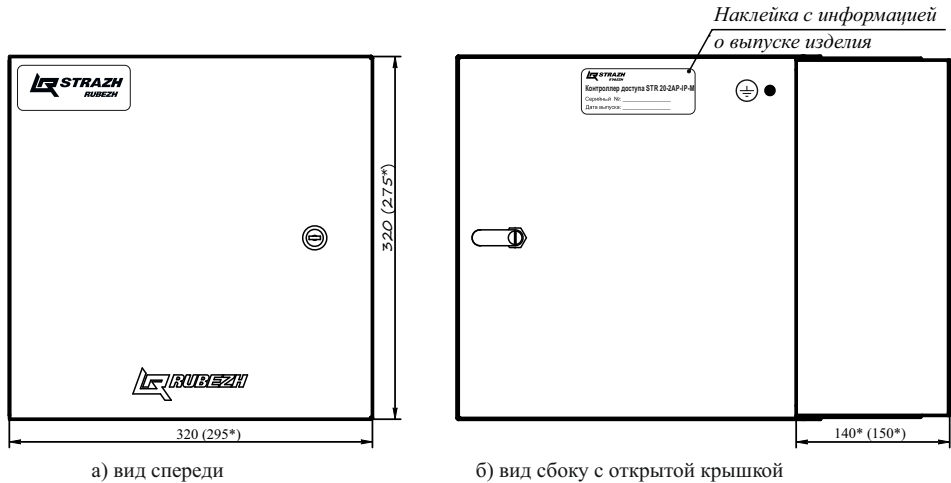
Внешний вид контроллера STR20-2AP-IP-M (*STR20-1AP-IP-M)
